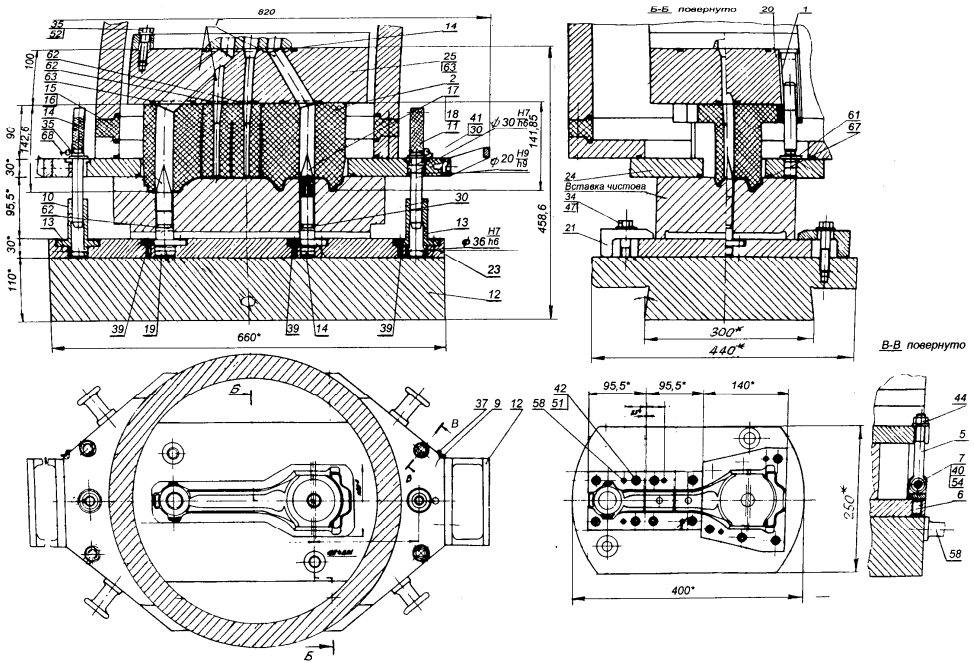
Пристрій для РОД порожнини рівчаквої вставки штампа КГШП для поковки «Шатун тракторний»
